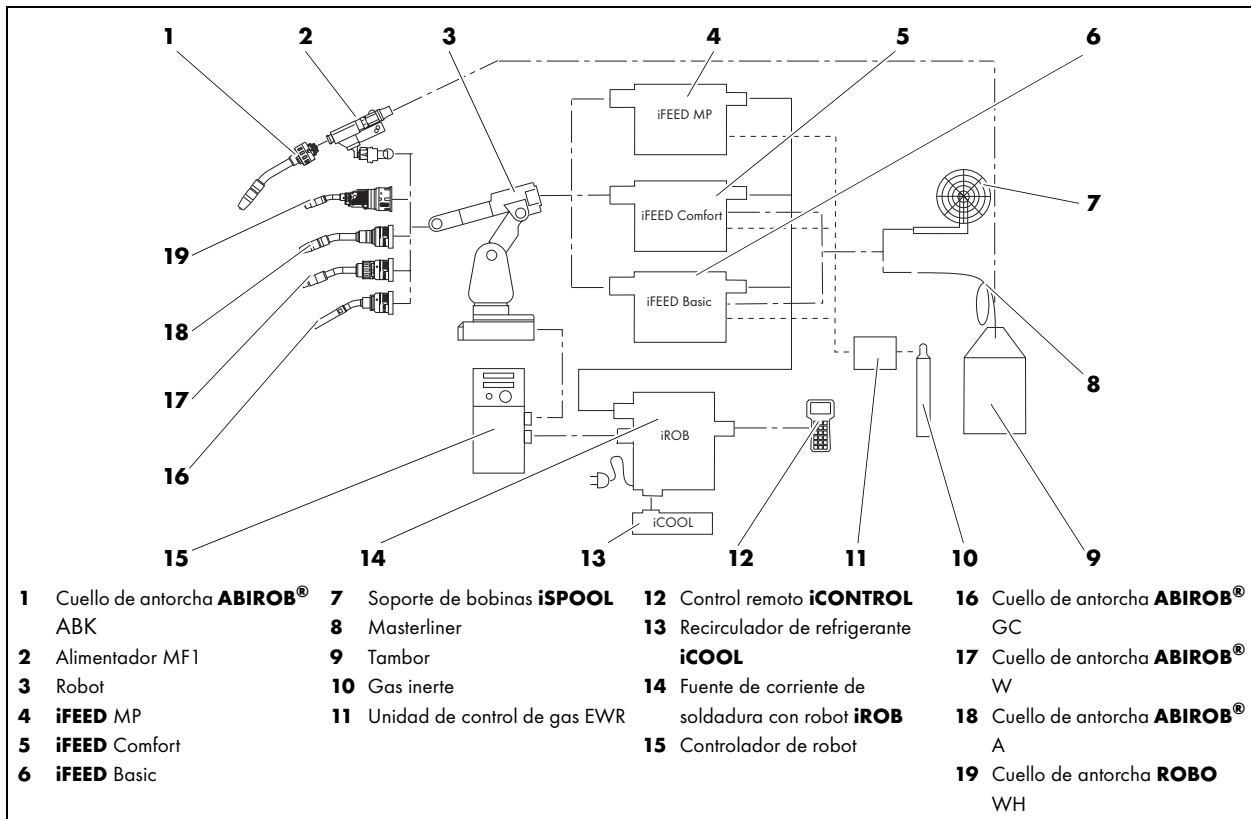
Componentes del equipo de soldadura con robot
